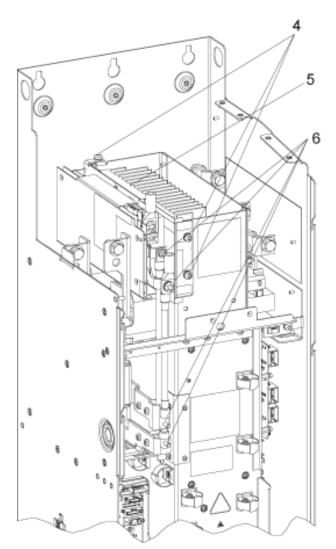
Montaje del Braking Module en un Power Module de tamaño FX: pasos 4 - 6
